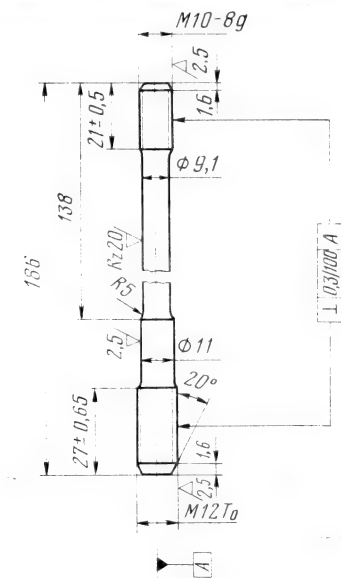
Шпилька крепления головок цилиндров (ремонтная) Сталь 40Х. Твердость HRC 23...29
